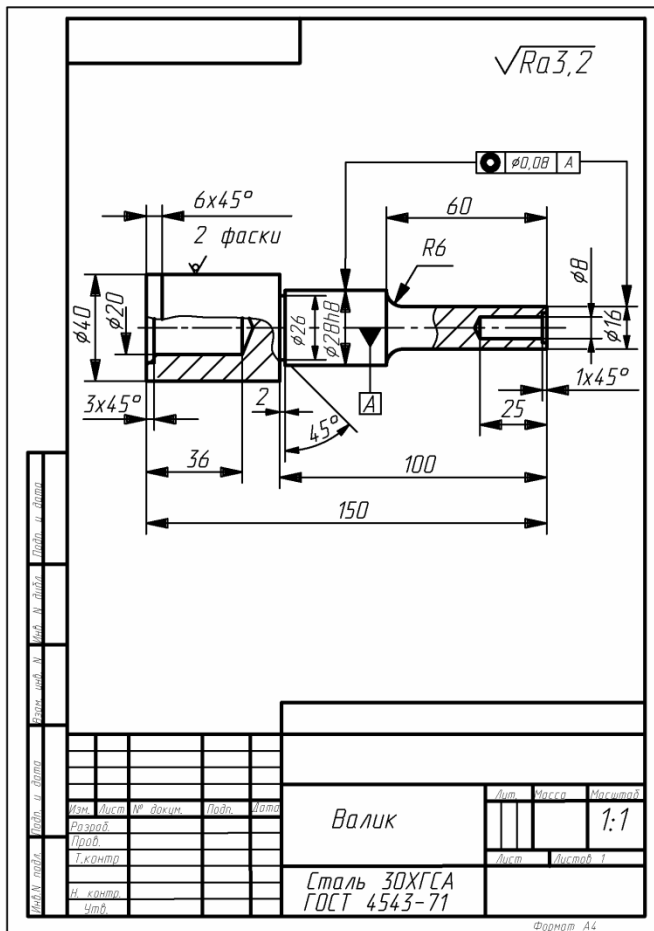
Приклад кресленника ступінчастого валіка
